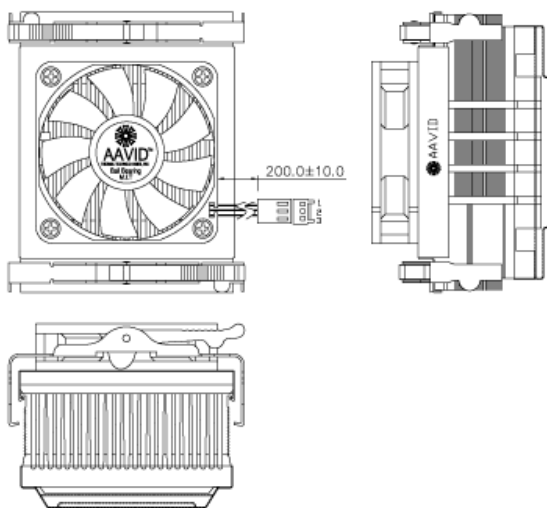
Desenho mecânico do dissipador 11-P4ES-01.
